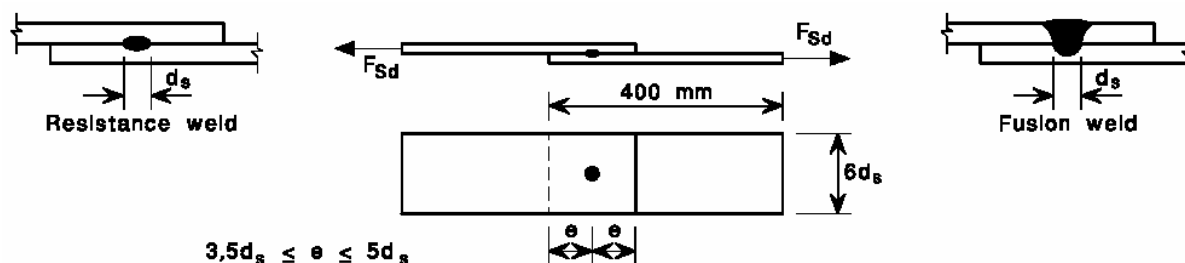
Образцы для испытаний на срез сварных точек
